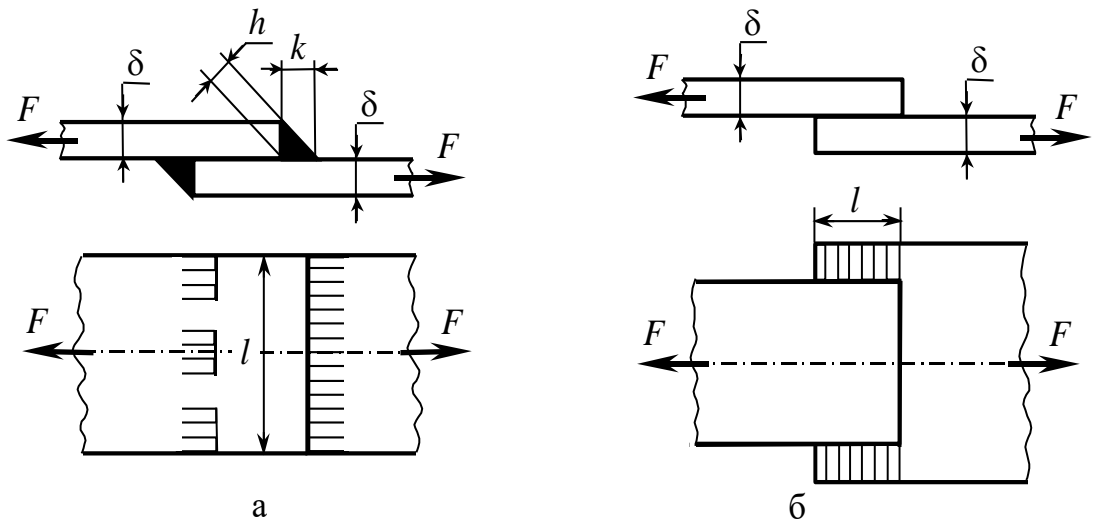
Розрахункова схема кутового зварного з'єднання
